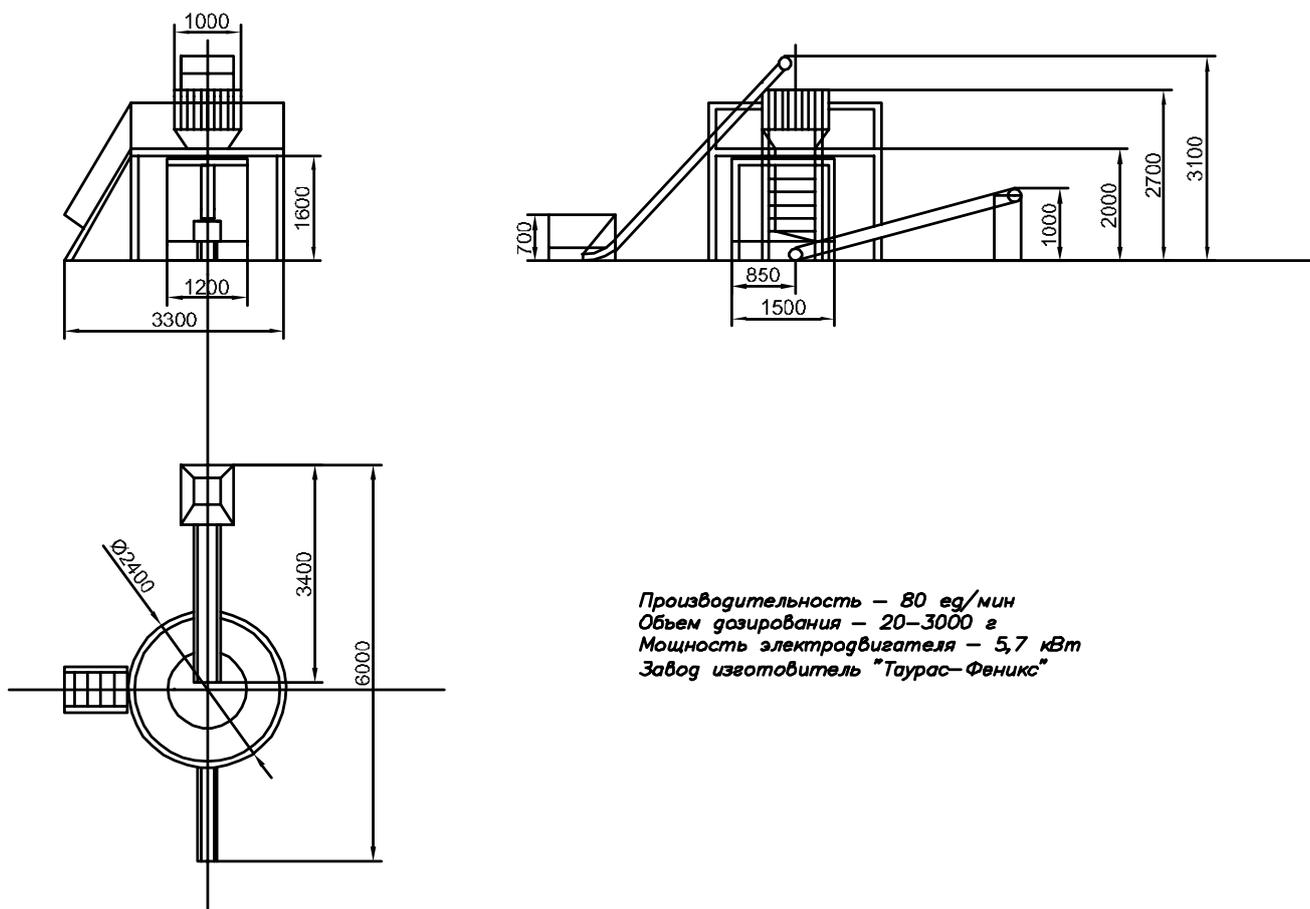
Фасовочно-упаковочный автомат «Питпак» для упаковки макаронных изделий
